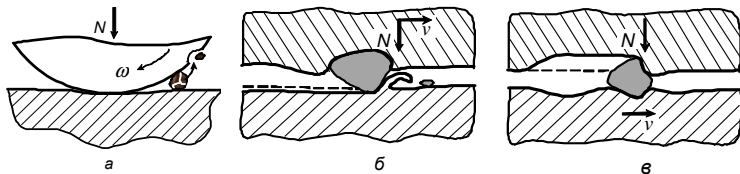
Механизмы изнашивания деталей свободными абразивными частицами
